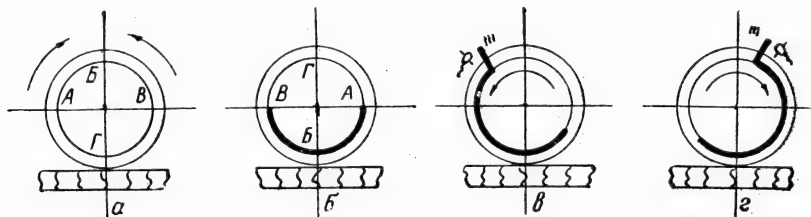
Последовательность работ при сварке поворотных стыков.
